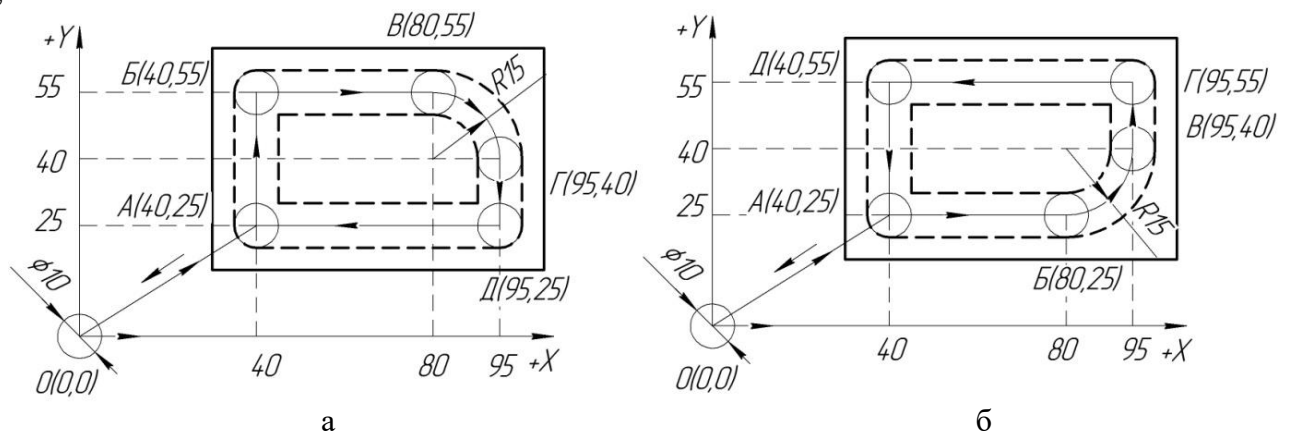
Фрезерування канавки по прямій і чверті кола за годинниковою (а) і проти годинникової стрілки (б)
